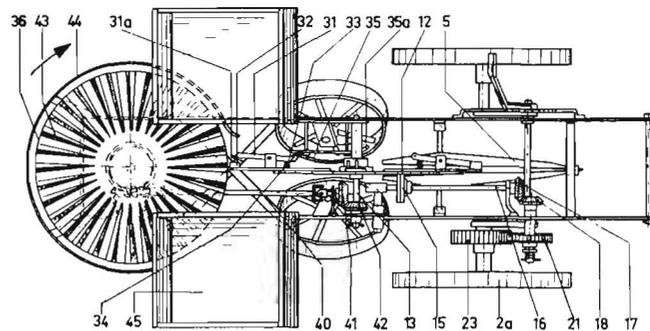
Pflanzensetzmaschine mit Einlegerteller
